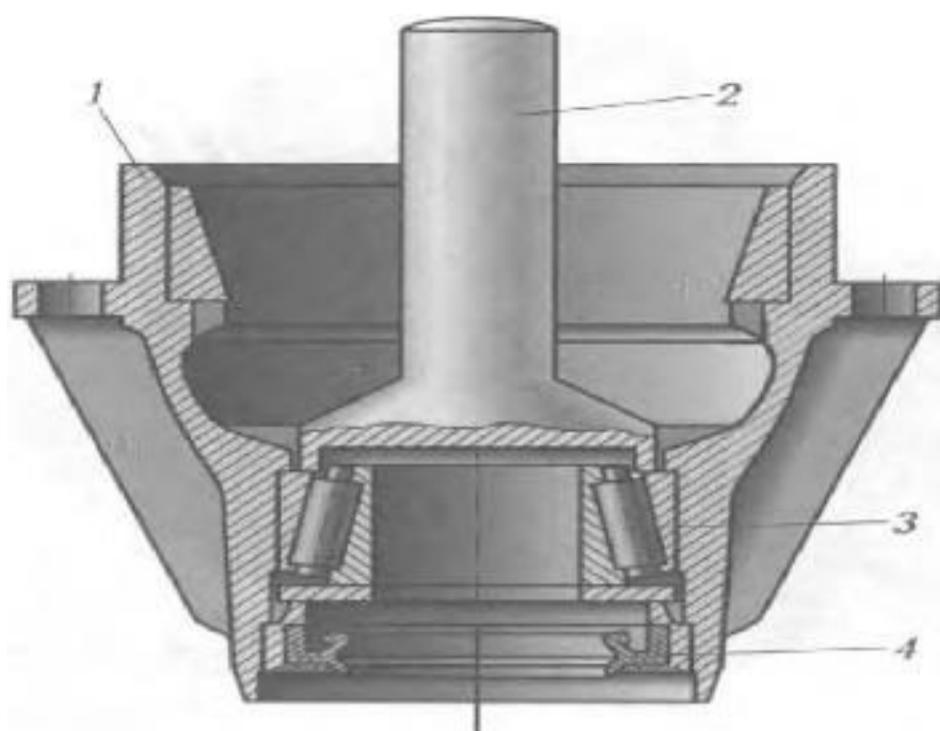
Выпрессовка обоймы в сборе с манжетой:
